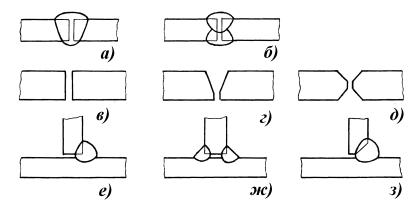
Подготовка кромок для выполнения сварных швов
